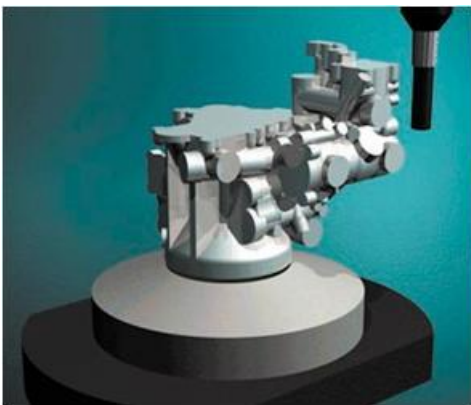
П'ятиосьова обробка дозволяє обробити всю деталь за один або два установи
